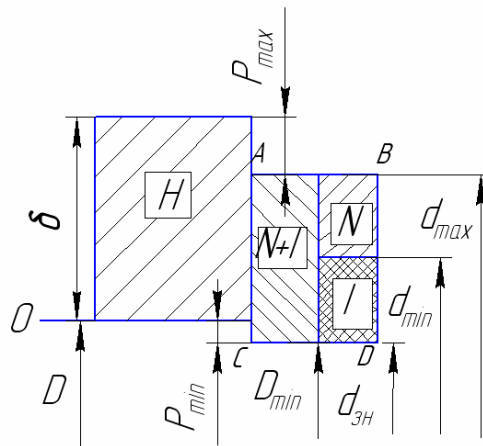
Розташування поля допуску розвертки
